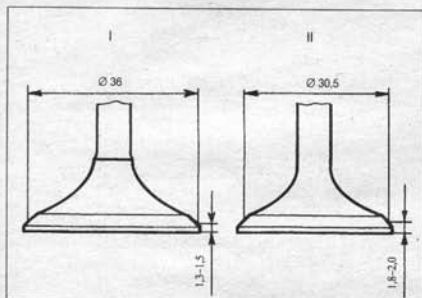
Предельные размеры при шлифовании фасок клапанов: I – впускного клапана; II – выпускного клапана
